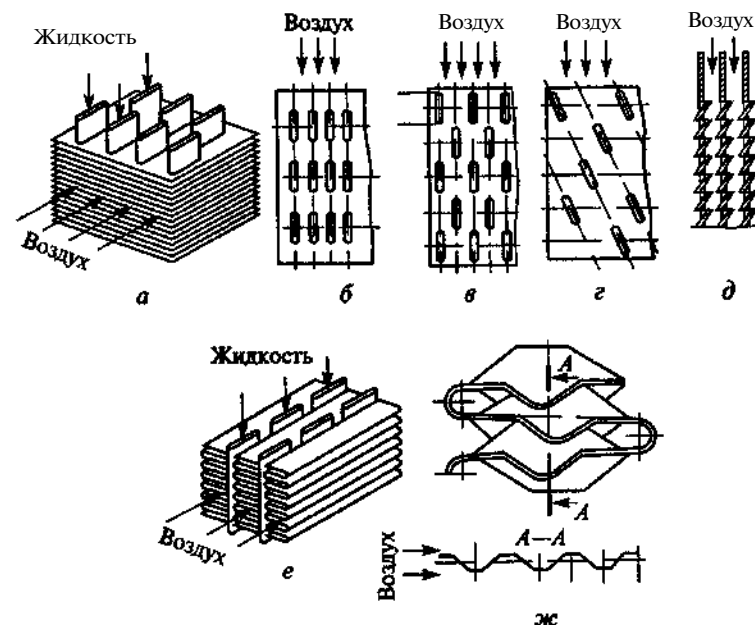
Решетки охлаждения трубчато-пластинчатых радиаторов (а — принципиальная схема; б — рядное расположение трубок; в — шахматное расположение; г — шахматное расположение под углом к воздушному потоку; д — охлаждающая пластина с отогнутыми просечками) и трубчато-ленточных радиаторов (е — принципиальная схема; ж — охлаждающая лента)
